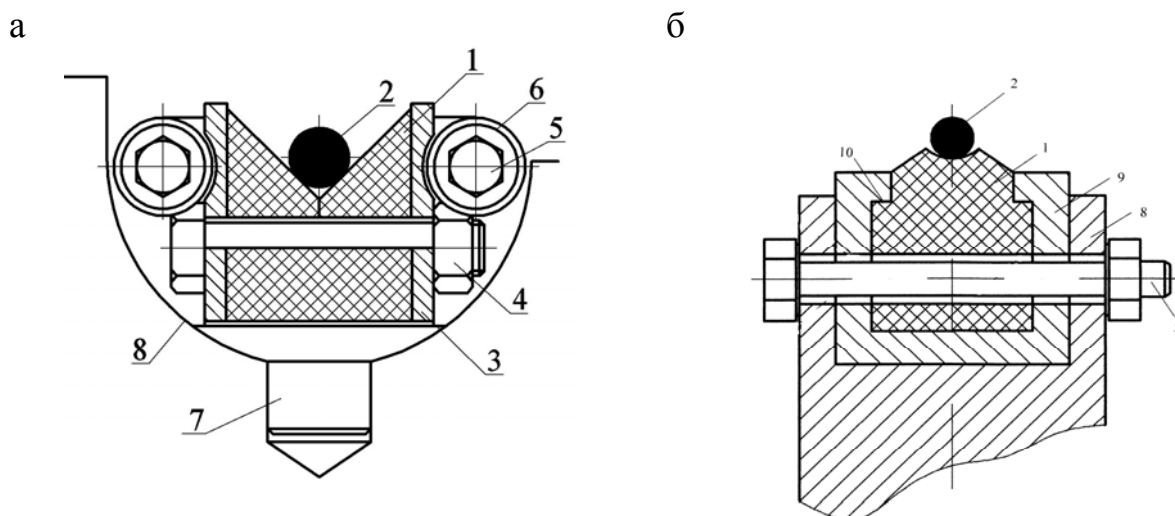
Приводной шкив трения с футеровкой(а – из резины; б – из материала Бекорит):1 - футеровка; 2 - канат; 3 - боковина; 4 - гайка; 5 - болт; 6 – проушина; 7 - шпонка; 8 – шкив; 9 – обойма; 10 – буртик
